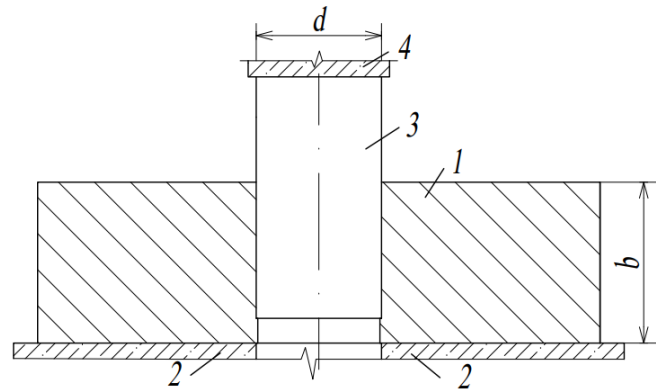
Комбінований спосіб дорнування: 1 – пластина; 2 – стіл випробувальної машини; 3 – робочий інструмент; 4 – рухомий затискач випробувальної машини (траверса) [128]
